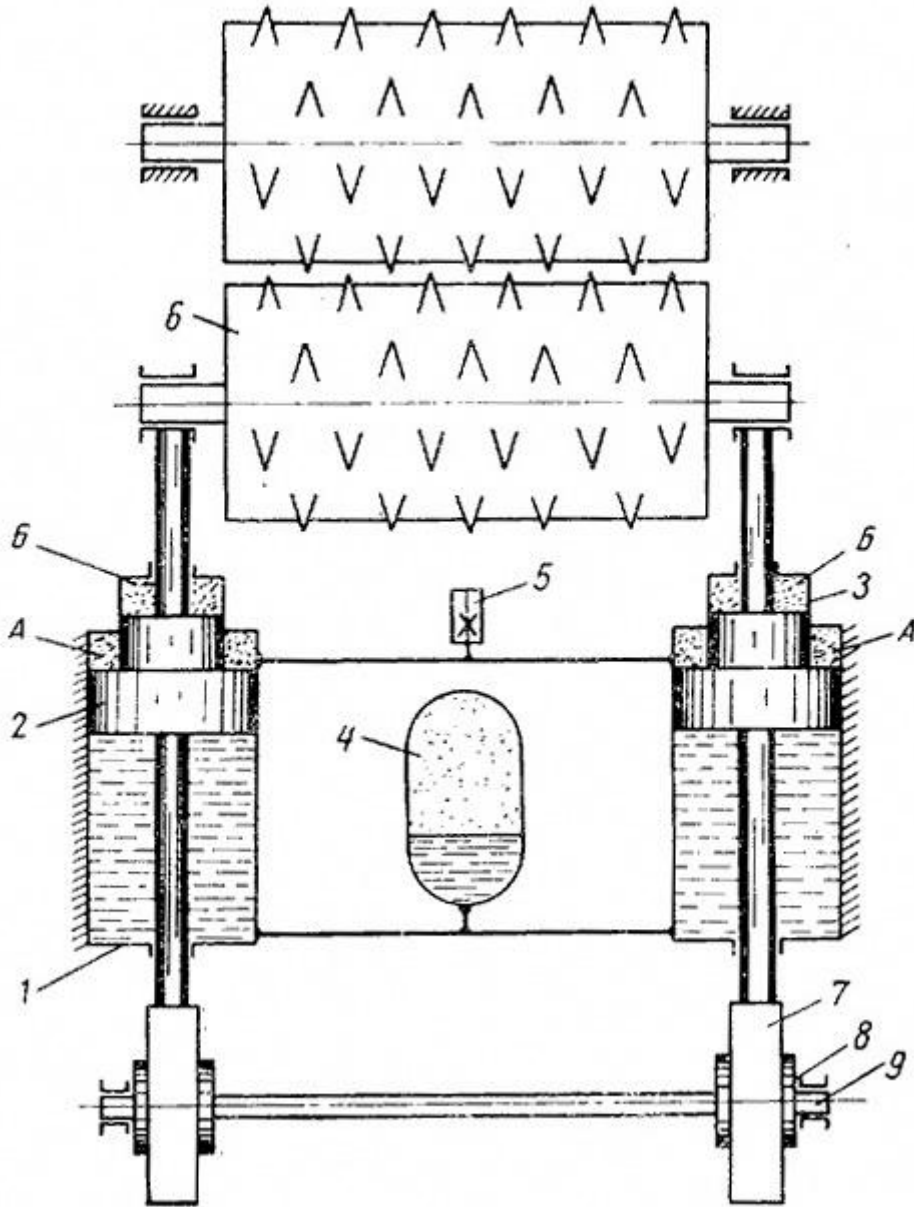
Гидропневматический амортизатор двухвалковой дробилки [7]:
